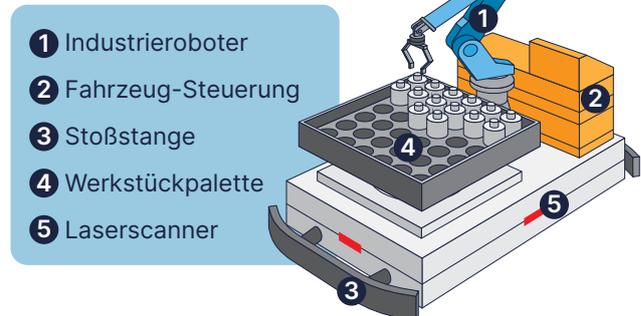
Fahrzeug mit Handhabungsroboter und Werkstückmagazin, basierend auf [2]
